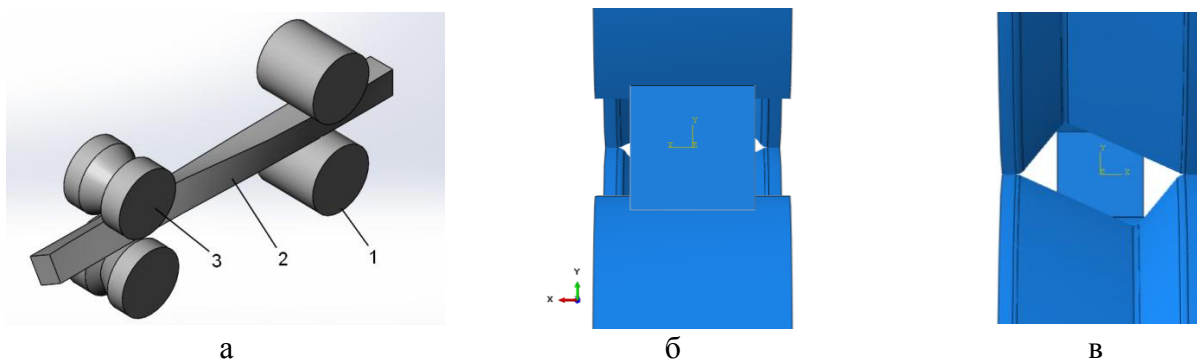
Технологічна (а) та розрахункова (б, в) схеми деформування металевої заготовки некруглого перерізу прокаткою з крученням (1 – заготовка; 2 – валки з гладкою бочкою; 3 – валки з каліброваною бочкою, рівчаки у вигляді трикутників):
